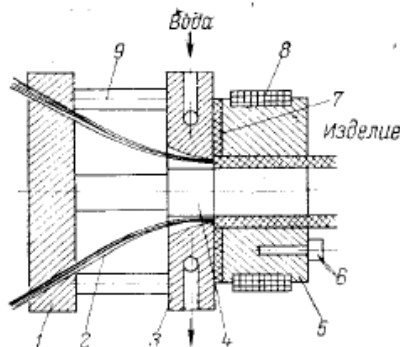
Формующая матрица агрегата для пултрузии труб.
